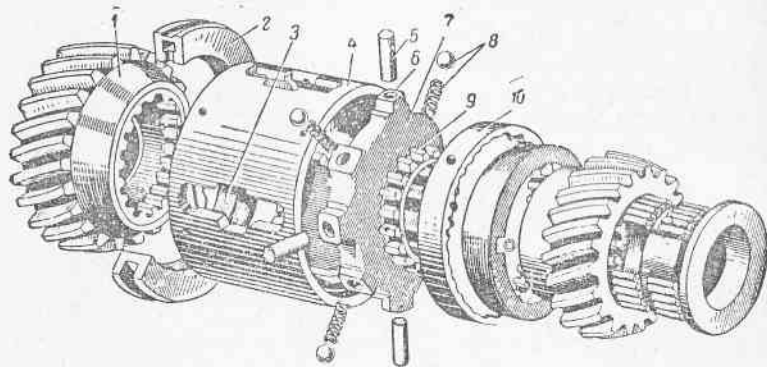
Синхронизатор коробки передач автомобиля МАЗ-200.
